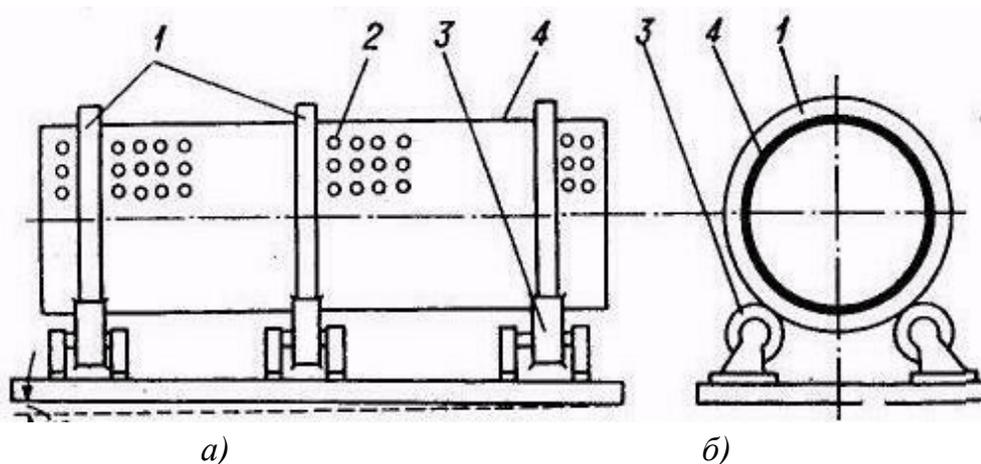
Цилиндрический барабанный грохот: а – вид сбоку; б – разрез; 1 – бандажи; 2 – отверстие; 3 – опорные ролики; 4 – барабан
